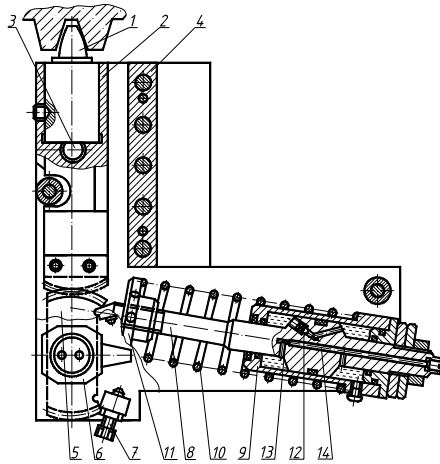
Устройство для обкатывания роликами клиноременных шкивов
